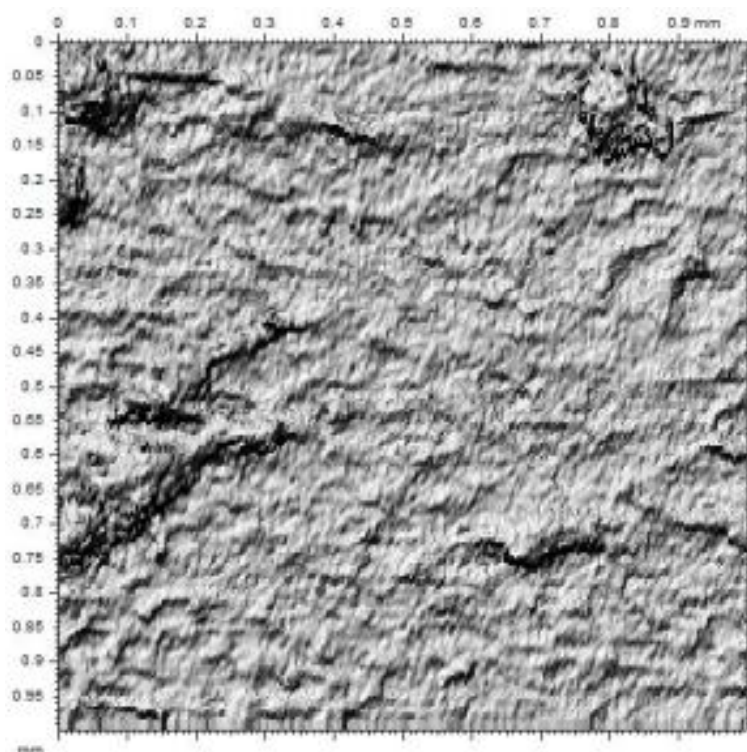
2D zobrazení broušeného povrchu oceli 19 436
